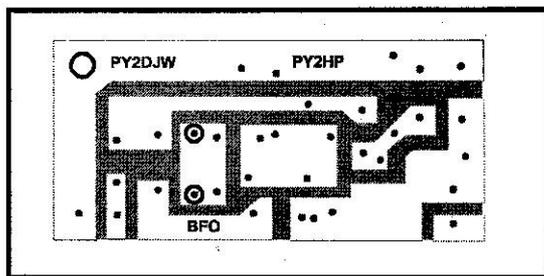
Plaqueta de circuito impresso, escala 1:1 (face cobreada), para a montagem do BFO.
